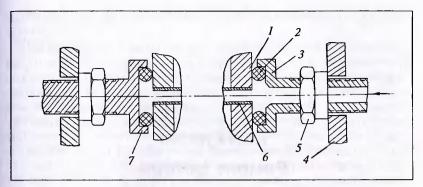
Гидравлические испытання трубок газоохладителей: 1— трубная доска; 2— резиновая кольцевая прокладка; 3— напорный штуцер; 4— швеллер-упор (закреплен к торцу газоохладителя); 5— упорная специальная гайка: 6— трубка газоохладителя: 7— штуцер-заглушка
